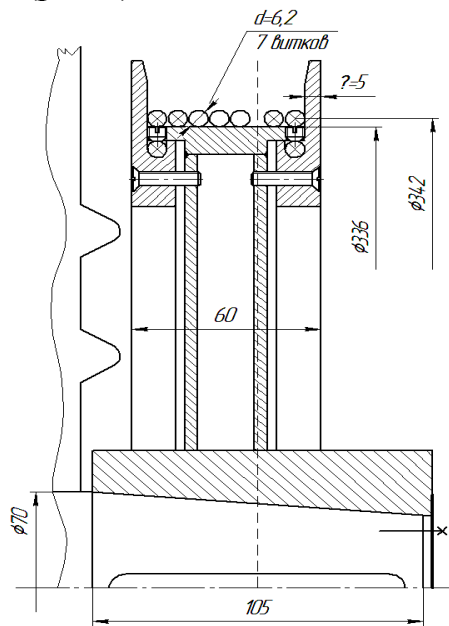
Барабан механизма передвижения с канатной тягой на валу редуктора Ч-125
